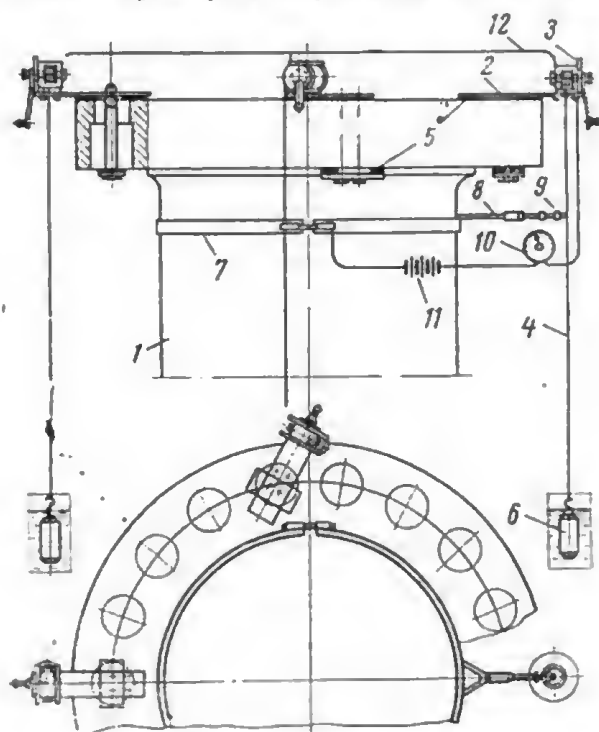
Приспособление для центровки вала турбины по струнам.
